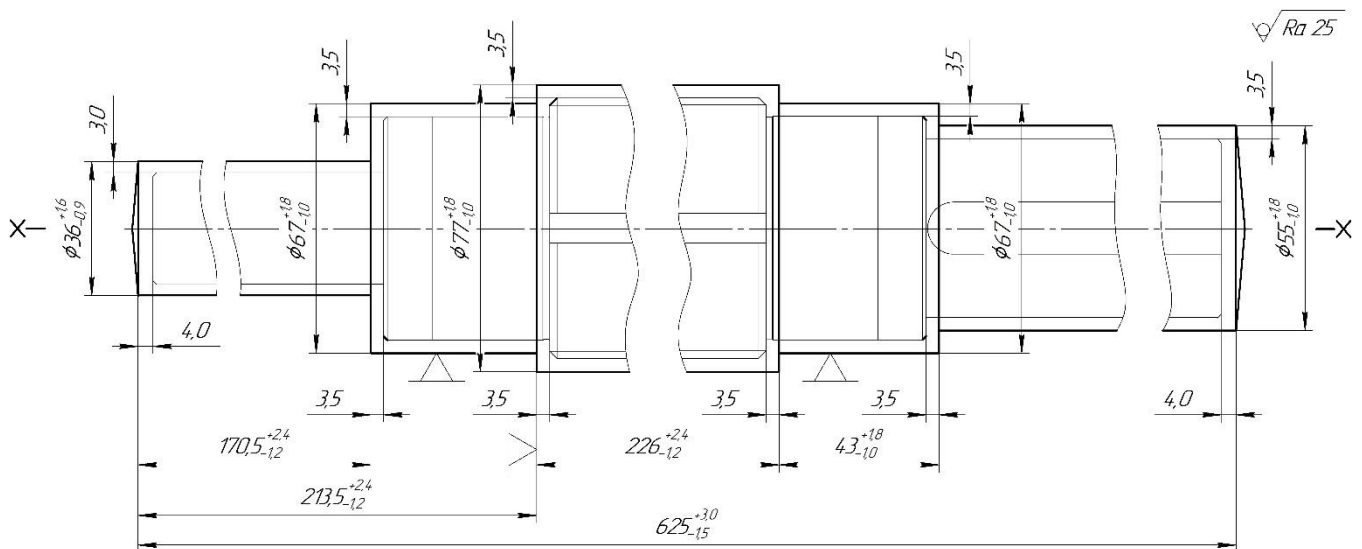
Заготовка, яка виготовлена штампуванням на КГШП
